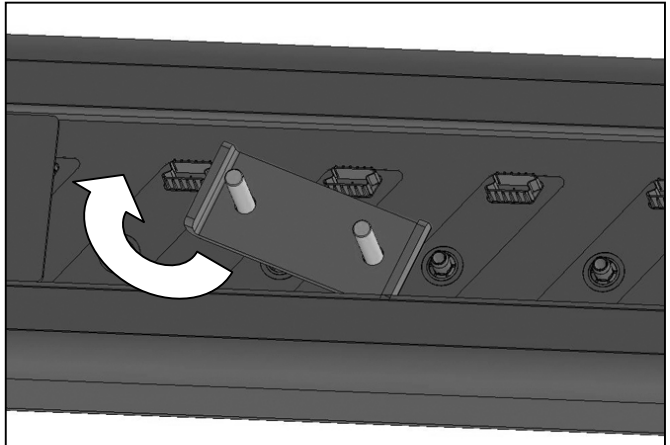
Ilustración del soporte posterior del lado del pasajero/derecho fijado al panel de la carrocería
